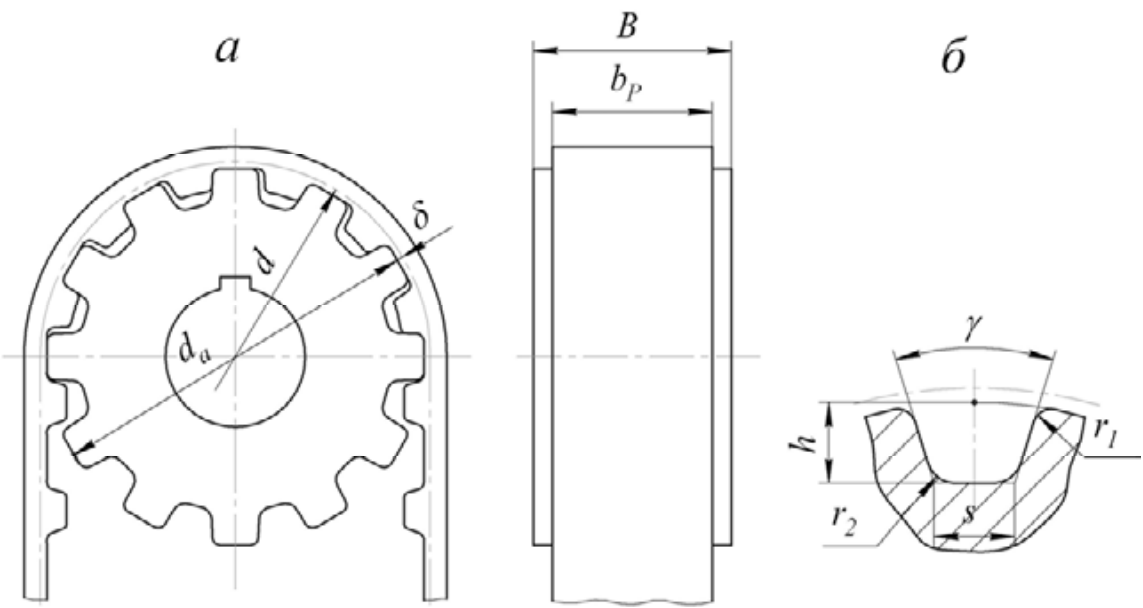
Шкив зубчато-ременной передачи с зубьями трапецеидального профиля (а) и профиль впадины (б)
